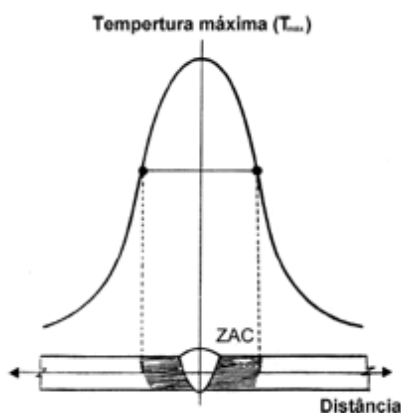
Seção transversal de uma junta soldada e sua repartição térmica[22].
